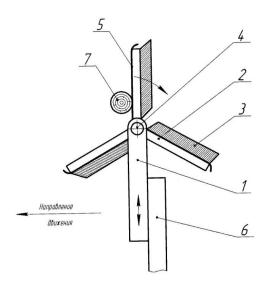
Схема устройства для обработки штамбовой зоны деревьев
